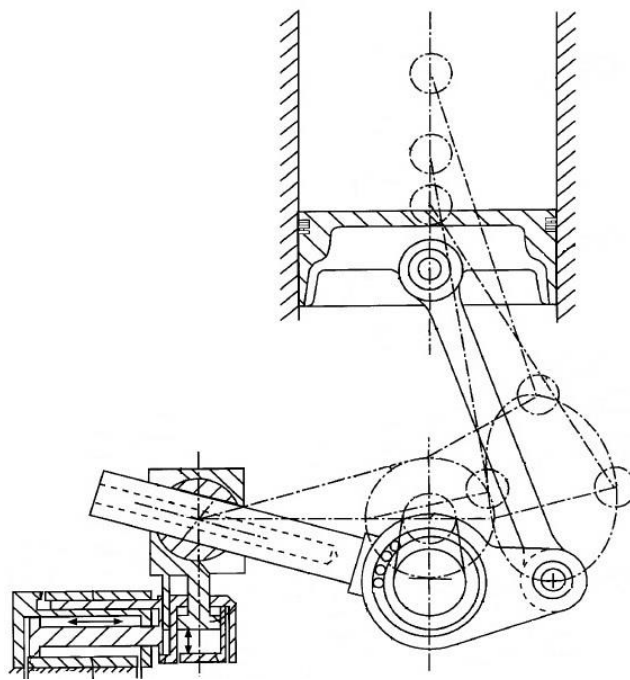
Розрахункова модель і схема двигуна Mayflower
